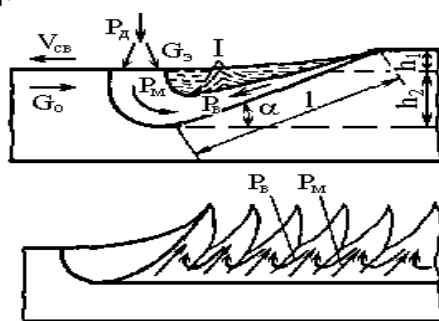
Схема образования всплесков в сварочной ванне и морщинистости на поверхности сварного шва
